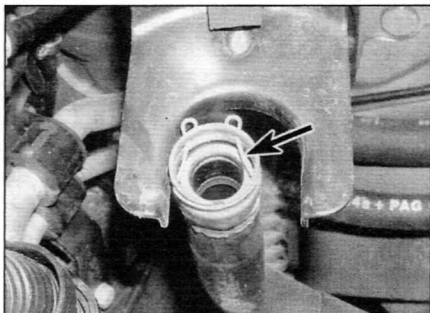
Перед подсоединением шланга установите уплотнительное кольцо и пружинный зажим
